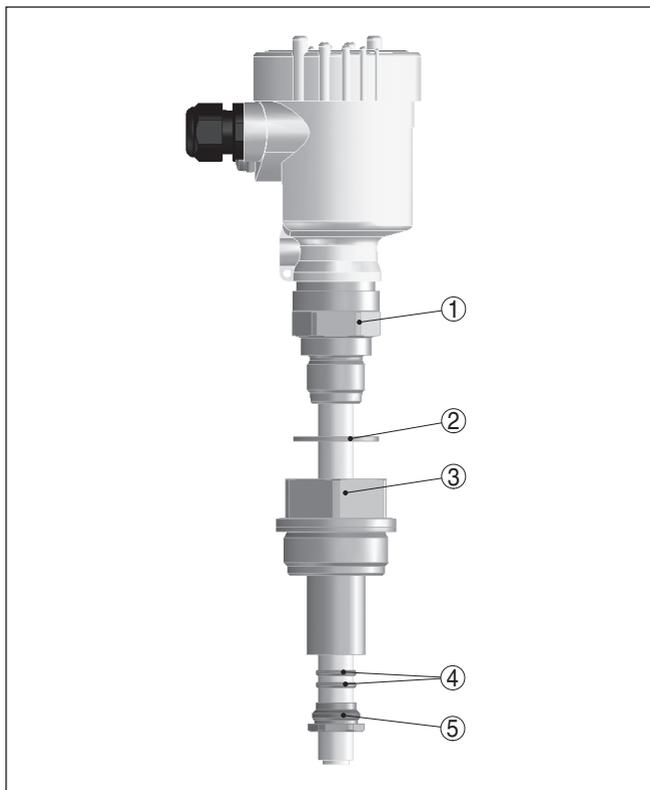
Montagem do adaptador com tubo de blindagem - Blindagem capacitiva, vedada por vácuo
